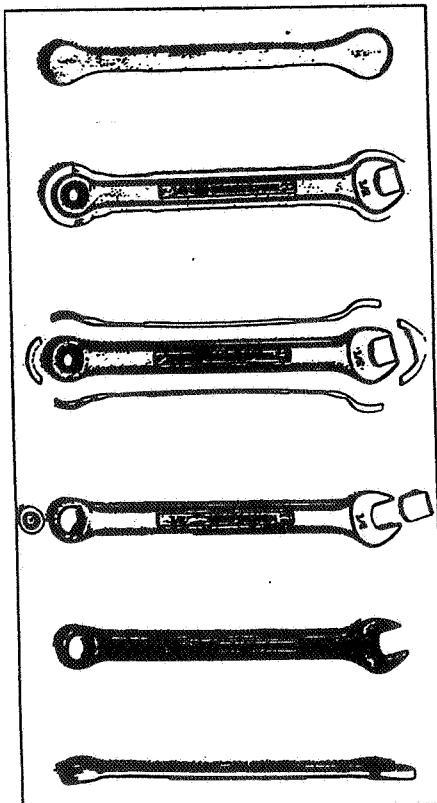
Le fasi di produzione mediante stampaggio a caldo di una chiave a forchetta.
